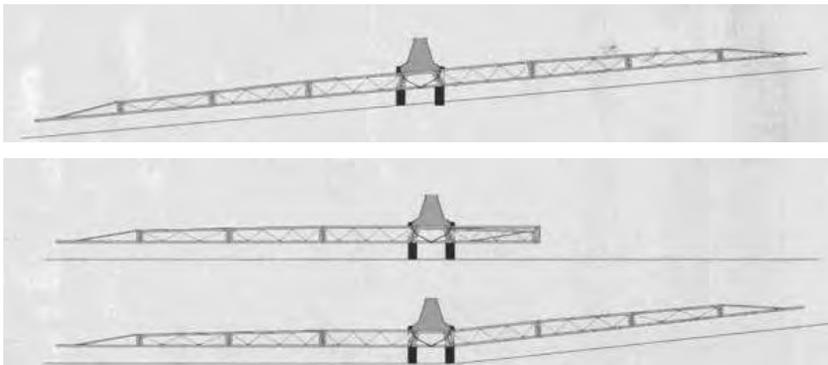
Схема изменения ширины захвата и угла установки штанги
